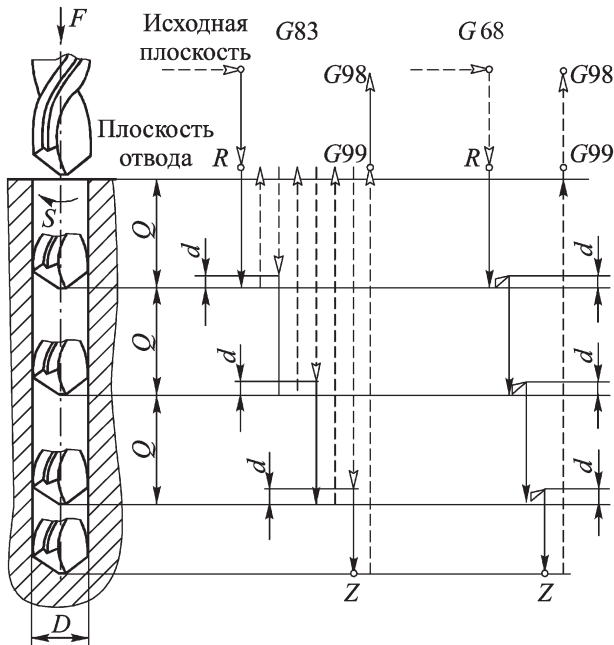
Циклы глубокого сверления на станках с ЧПУ
